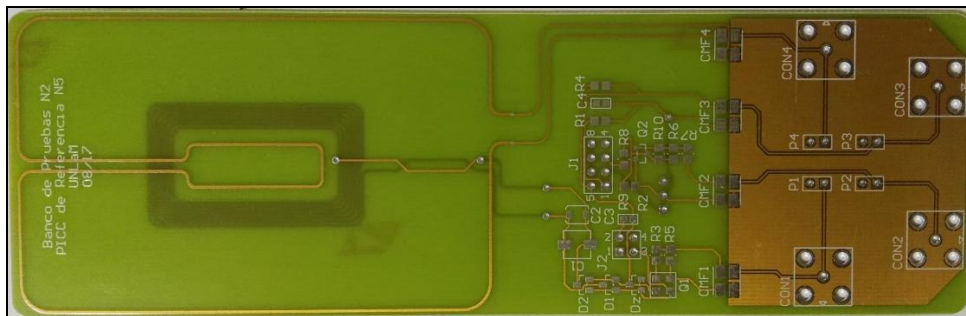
PCB PICC de Referencia N° 5 – Capa TOP
